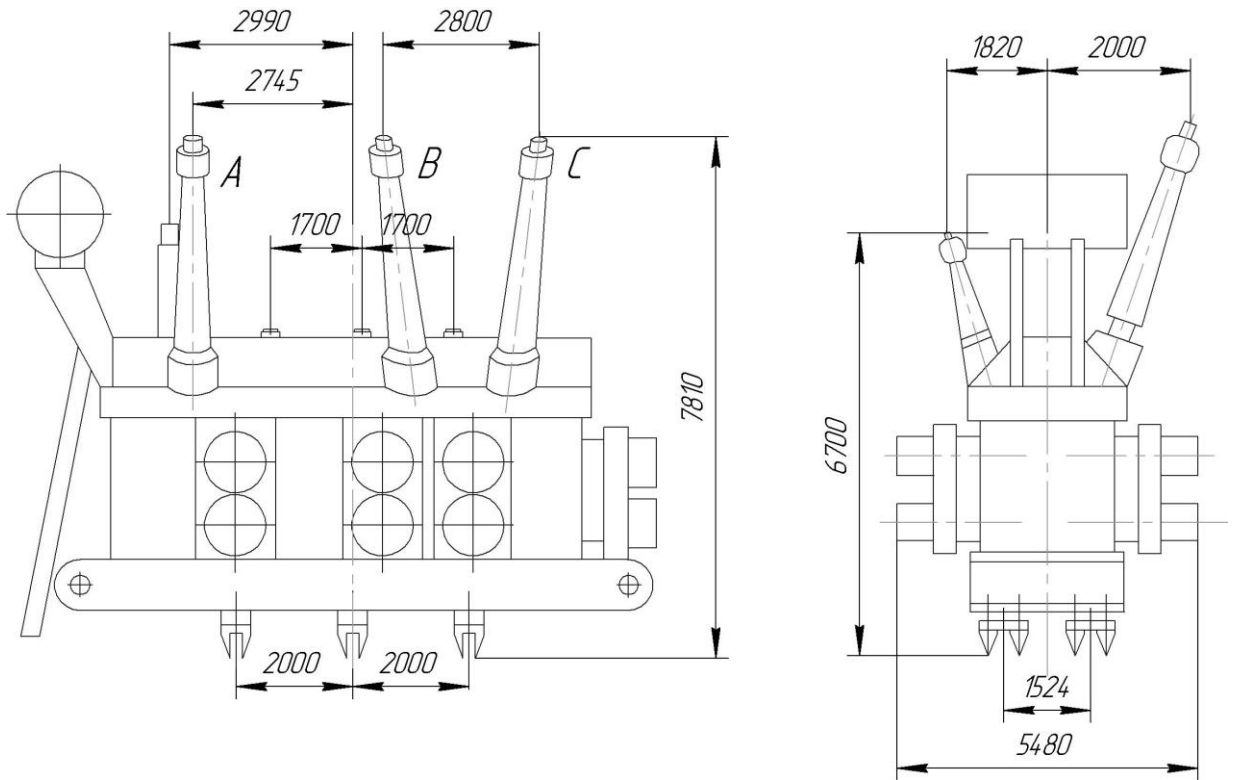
Габаритный чертеж автотрансформатора
